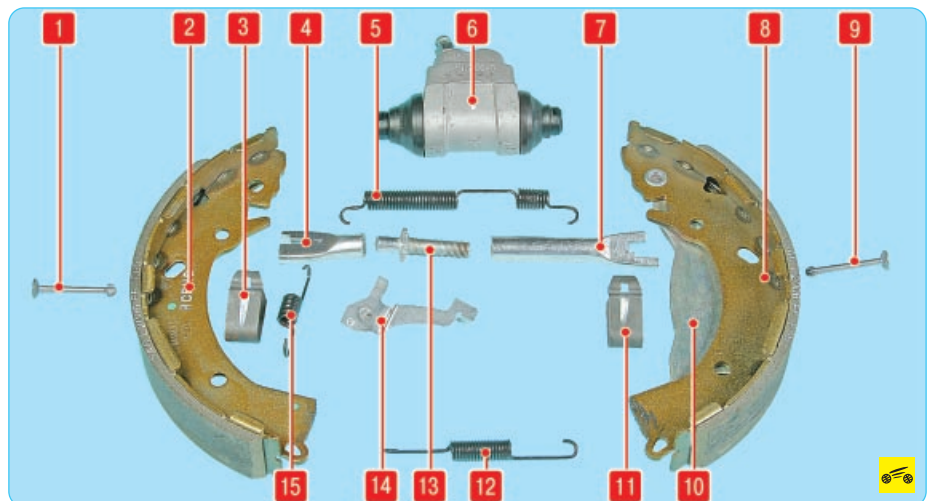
Детали барабанного тормозного механизма заднего колеса (показаны детали тормозного механизма с левой стороны): 1, 9 – стержни опорных стоек колодок; 2 – передняя колодка тормозного механизма; 3, 11 – пружинные пластины; 4 – передняя часть распорной планки; 5 – верхняя стяжная пружина колодок; 6 – рабочий тормозной цилиндр; 7 – задняя часть распорной планки; 8 – задняя колодка тормозного механизма; 10 – разжимной рычаг привода стояночного тормозного механизма; 12 – нижняя стяжная пружина; 13 – регулятор зазора; 14 – рычаг регулятора зазора; 15 – пружина рычага регулятора зазора
